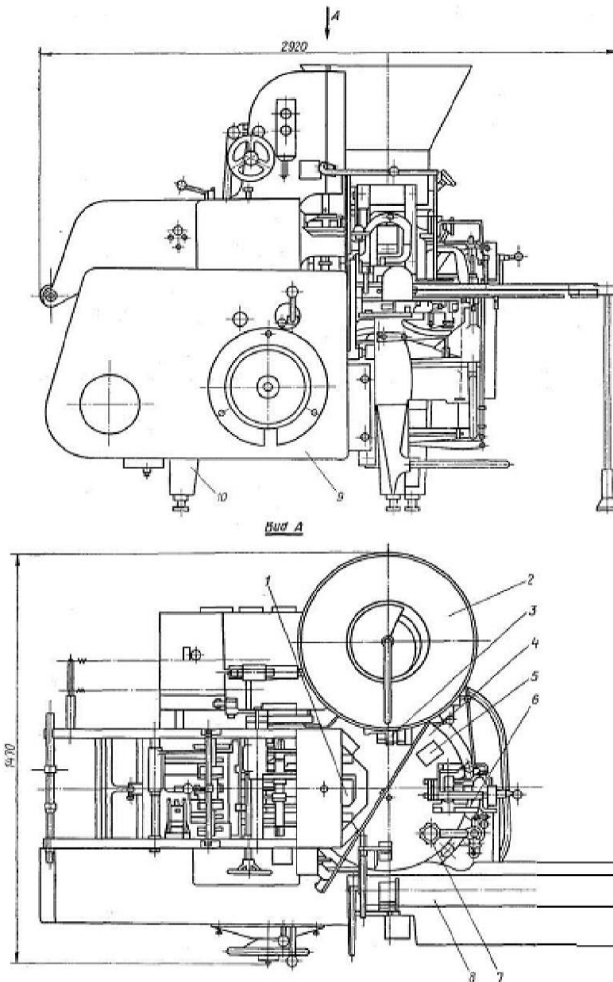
Автомати М6-АРС, М6-АР1С: 1 - матриця пакетоутворювача; 2 - бункер; 3 - дозатор; 4 - формувальний стіл; 4 - маховик регулювання продуктивності; 5 - гніздо формувального стола; 6 - механізм загортання пакета; 7 - механізм підпресування; 8 - транспортер; 9 - станина з головним приводом; 10 - опорна ніжка
